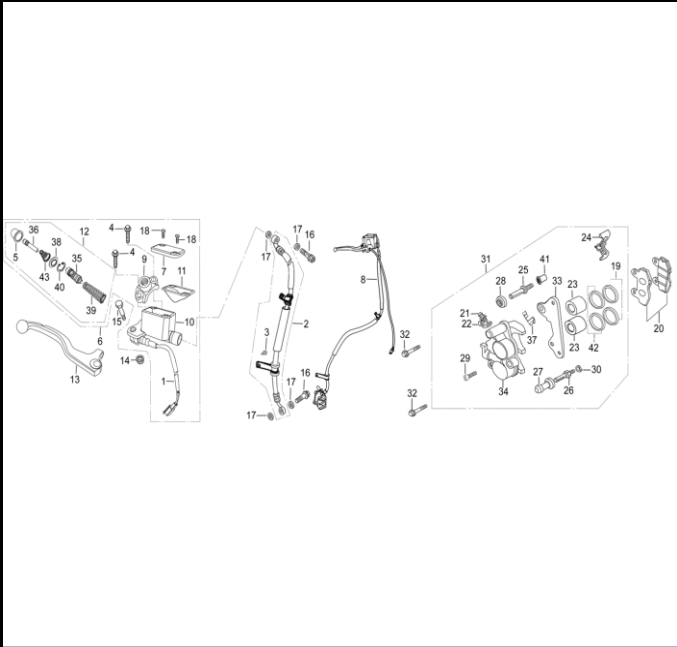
BOMBA FRENO DELANTERO - CALIPER DELANTERO
